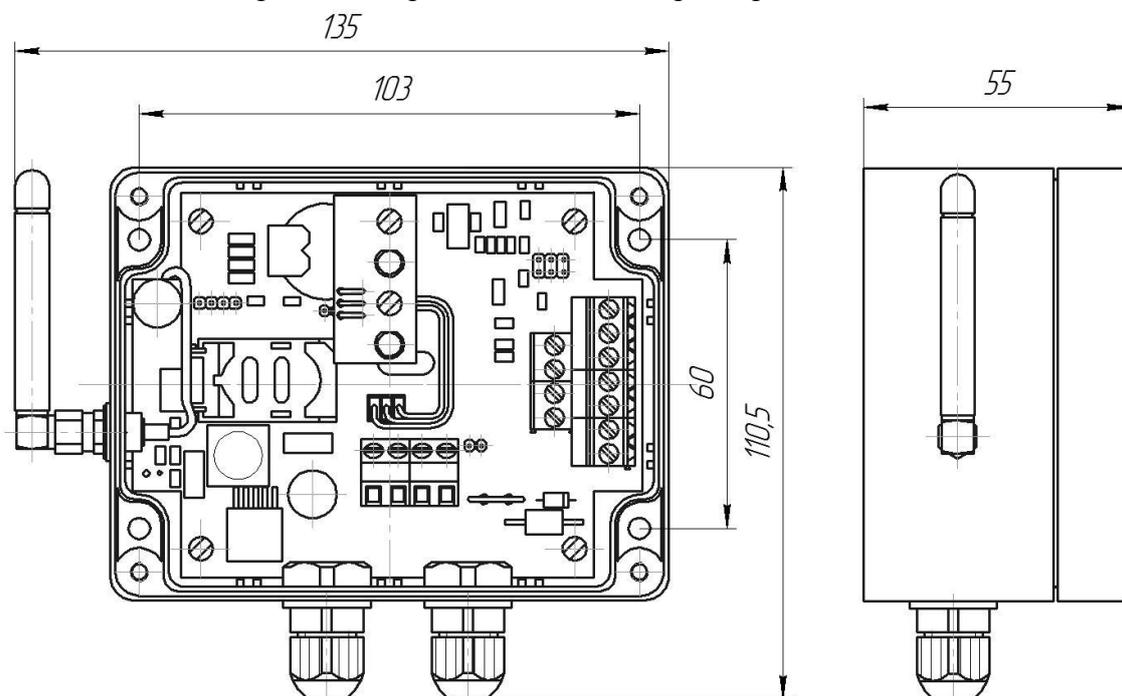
Габаритные и присоединительные размеры терминала «БАРС-01-Т».
